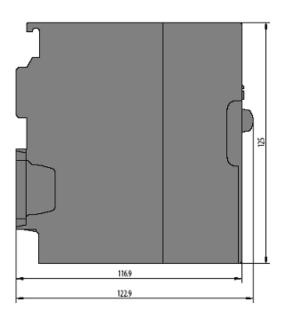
Dimensiones técnicas de la CPU 314C-2DP
